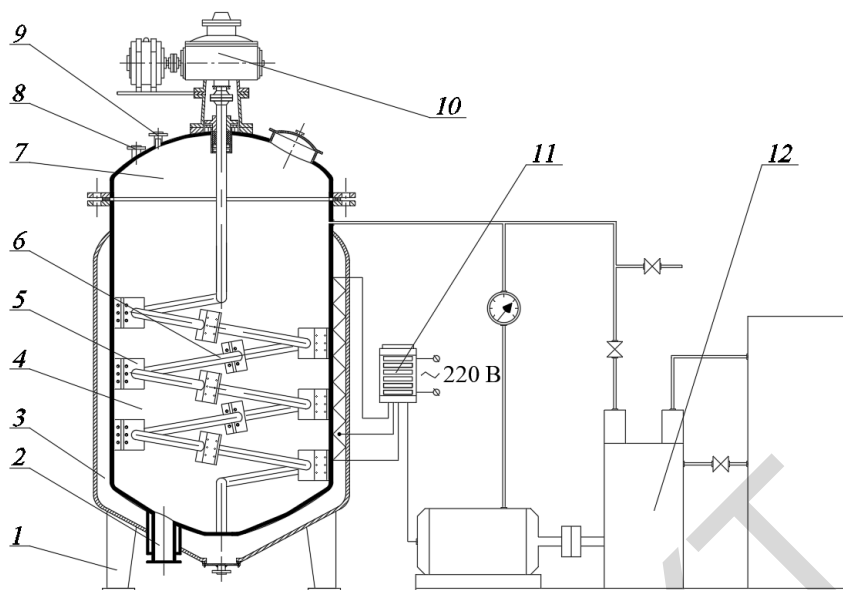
Установка для уварювання овочевої сировини під вакуумом при постійному перемішуванні: 1 – опори; 2 – патрубок для зливання готового продукту; 3 – парова сорочка; 4 – робоча камера апарату; 5 – скребок перемішуючого пристрою; 6 – вал мішалки; 7 – кришка апарату; 8 – патрубок для відведення вологи; 9 – патрубок для подачі сировини; 10 – електродвигун; 11 – блок керування робочими процесами апарату; 12 – система вакуумування апарату.
